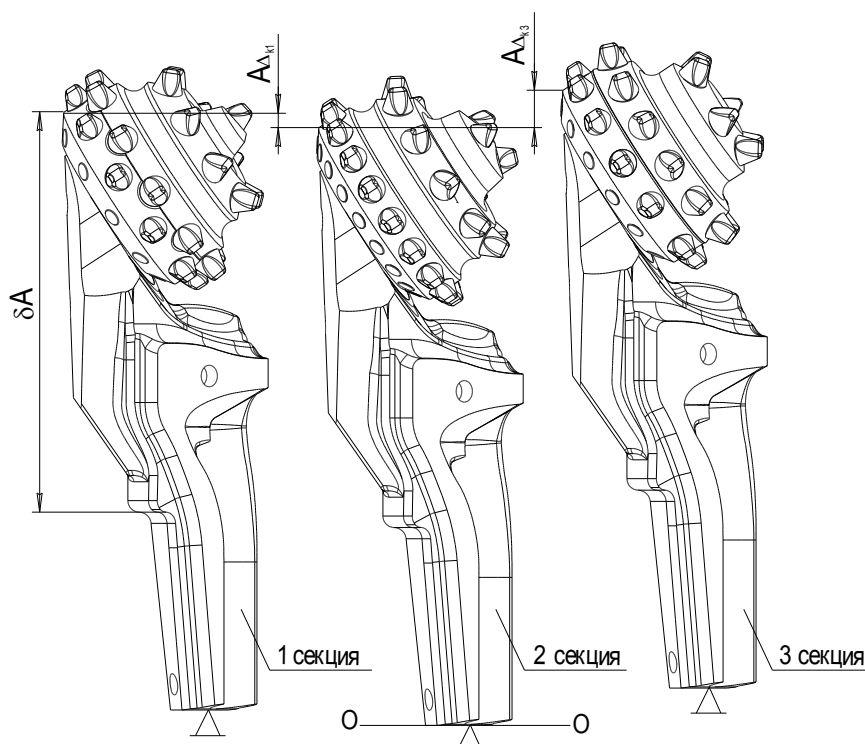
Замыкающие звенья размерной цепи сборки секций под сварку
